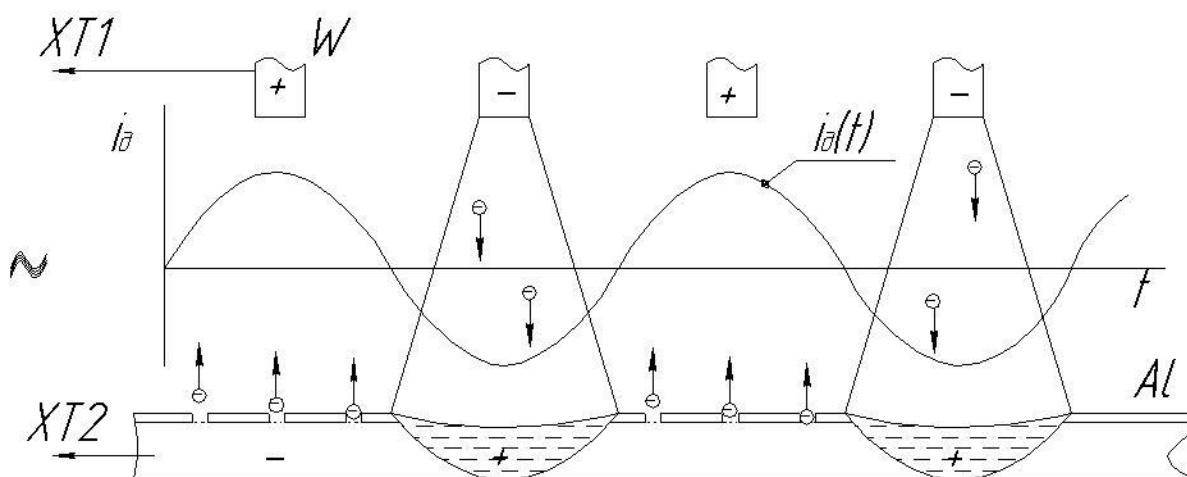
Схема разрушения окисной пленки при сварке алюминиевых сплавов на переменном токе
